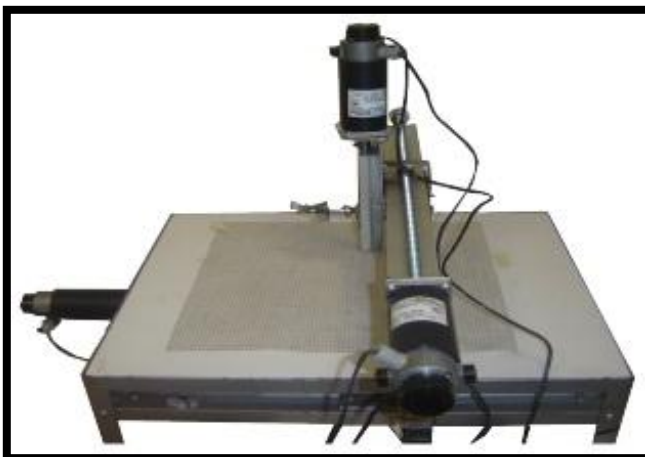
Mesa Posicionadora Universidad Mixteca [8]
